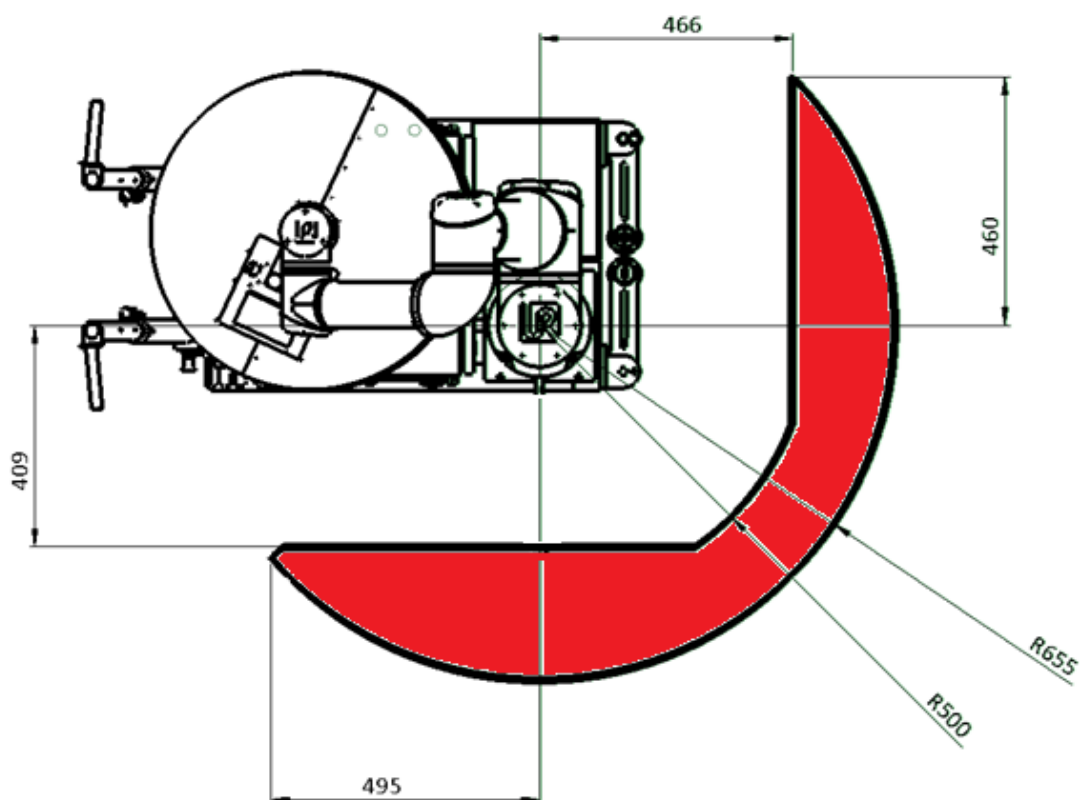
Maximální úhel alfa a beta robotu Universal robots UR 16E
